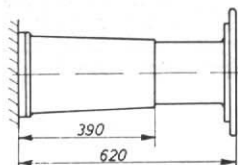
Stoßpuffer mit 15-t Doppel-Evolutfeder für kurzgekuppelte Fahrzeuge.
